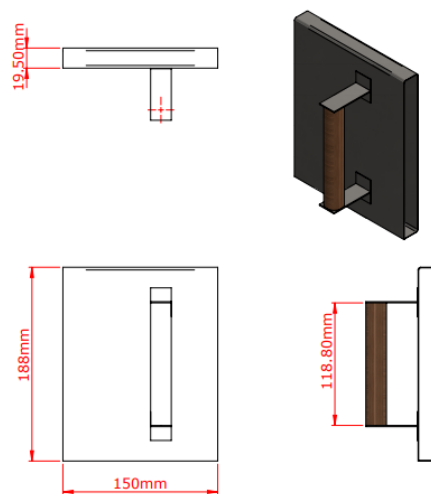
Sección 1 de la puerta - Detalle de las medidas
